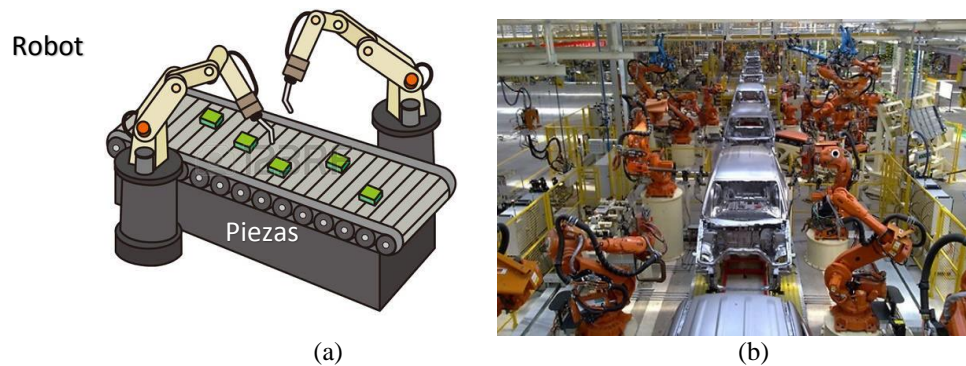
(a) Esquema robot en línea, (b) aplicación, soldadura automotriz
